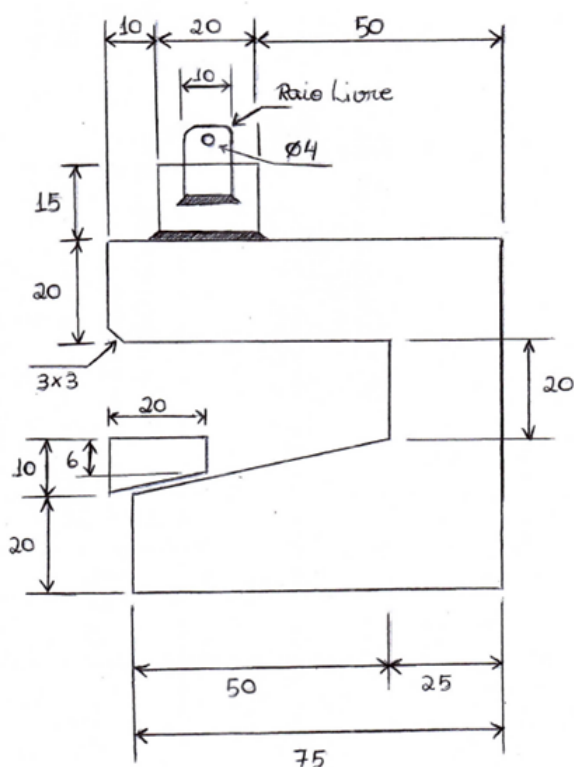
Projeto de detalhamento para fabricação da garra superior.
